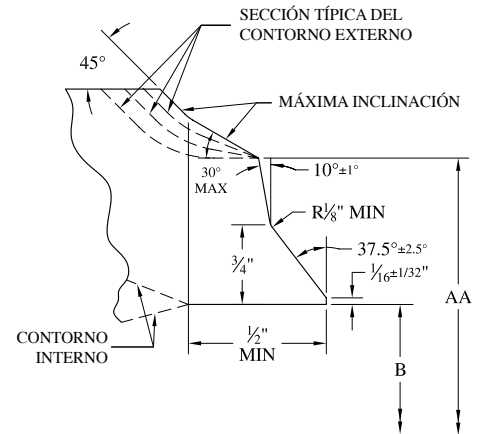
B - Extremo soldable para ensamblar con arillo de respaldo bipartido para espesores de tubería mayor a "t" 7/8"
